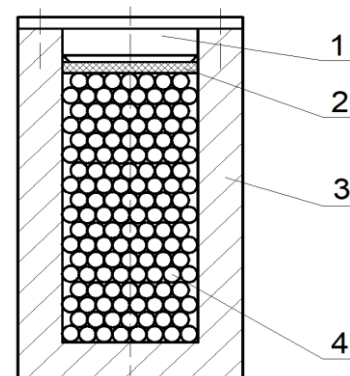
Схема бабы с наполнителем: 1 – крышка; 2 – упругая прокладка; 3 – корпус; 4 – шарики
